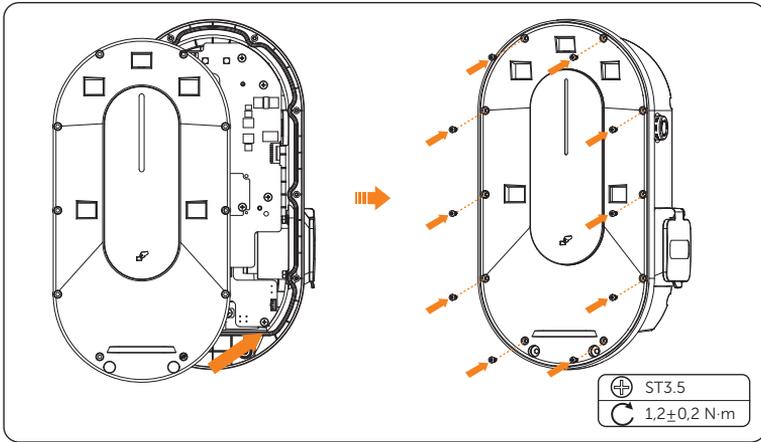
Frontplattenabdeckung wieder anbringen
